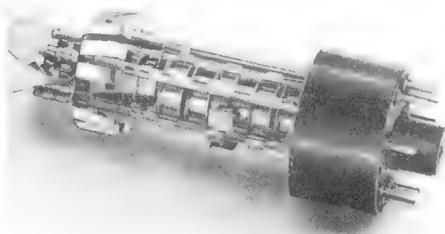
System der DG 13-14. Die einzelnen Elektroden sind auf vier Keramiksäulen aufgereiht und verschweißt
